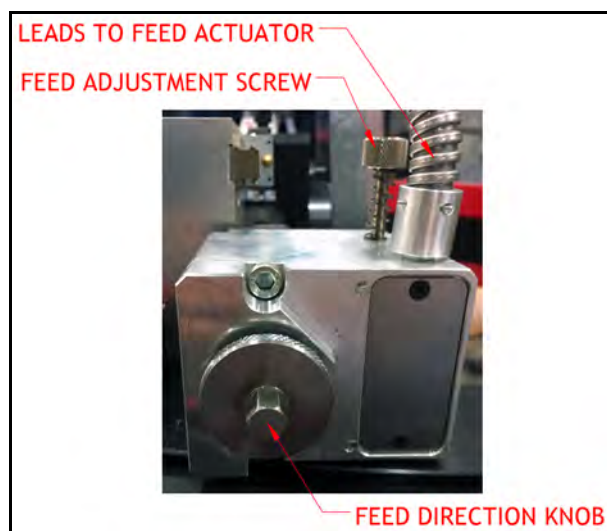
РЕГУЛИРОВКА ПОДАЧИ
